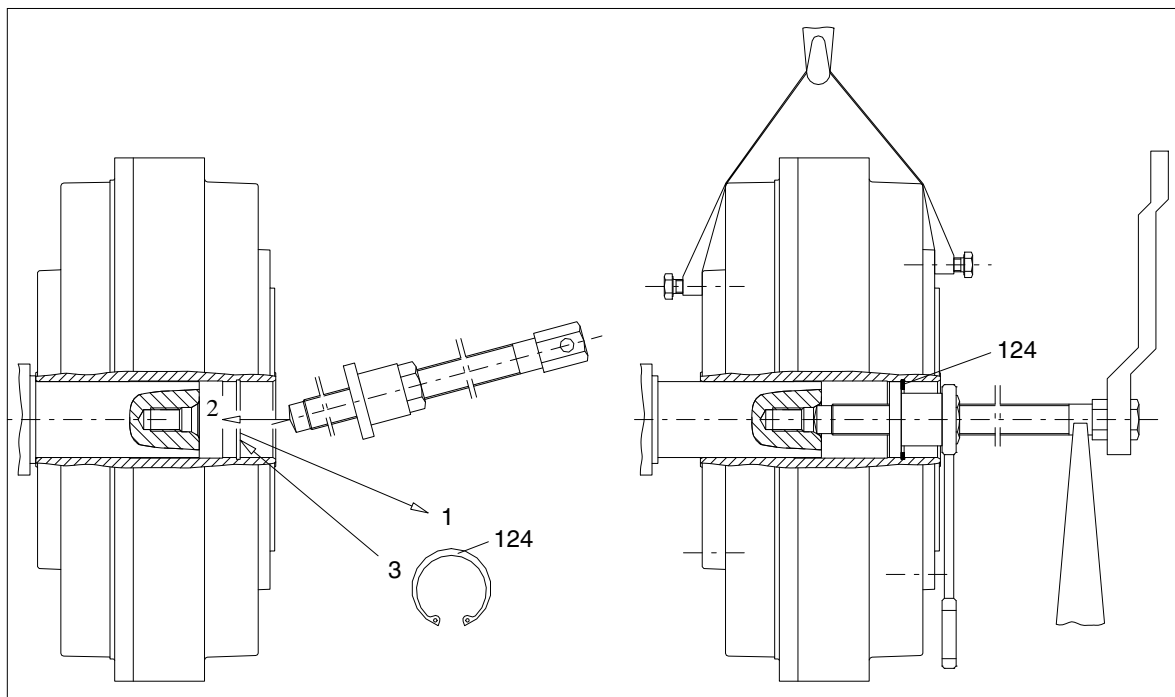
Smontaggio delle grandezze 297 e 342 - b
